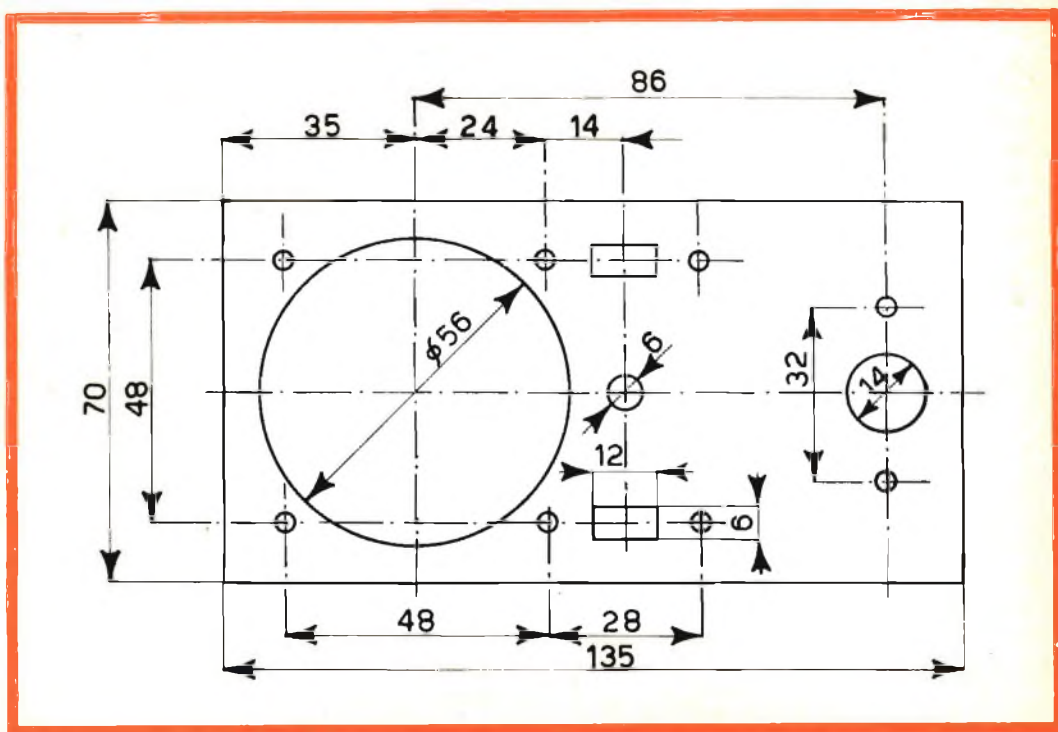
Piastrina di supporto, le dimensioni sono state indicate in millimetri. Tutti i fori minori hanno il diametro di 35 mm.
